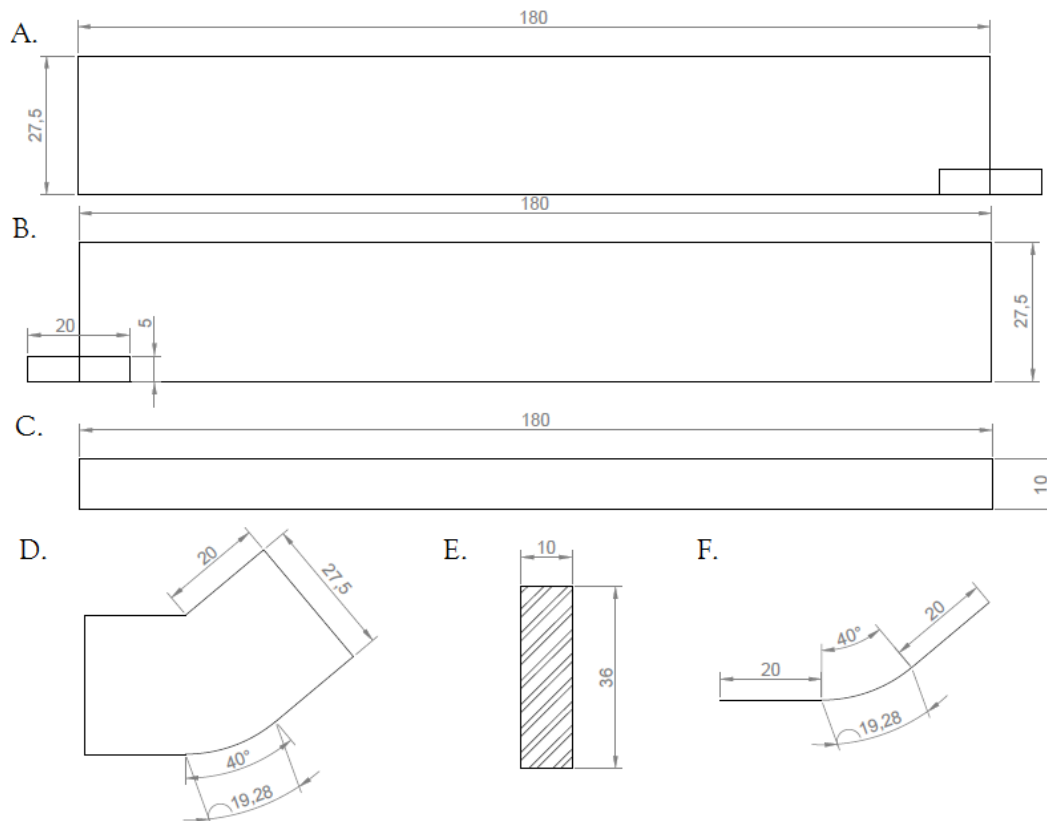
Detalle de las piezas componentes del canal Collapses V1.0: A. Piezas 1 y 2, B. Piezas 3 y 4, C. Piezas 7 y 8, D. Piezas 5 y 6, E. Pieza 9, F. Pieza 10
